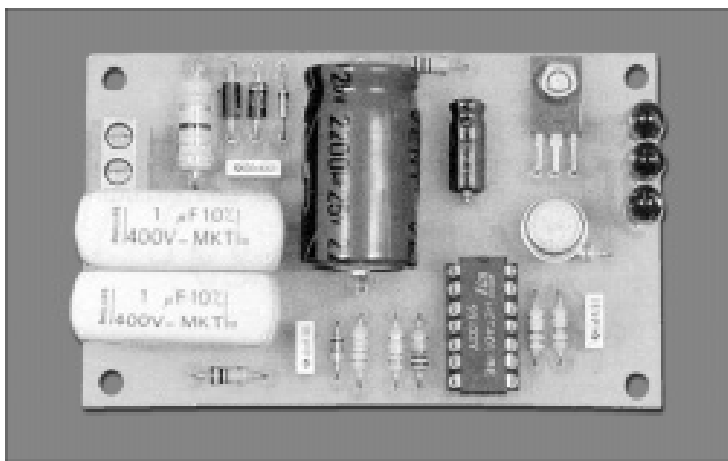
Общий вид излучателя инфракрасного барьера
